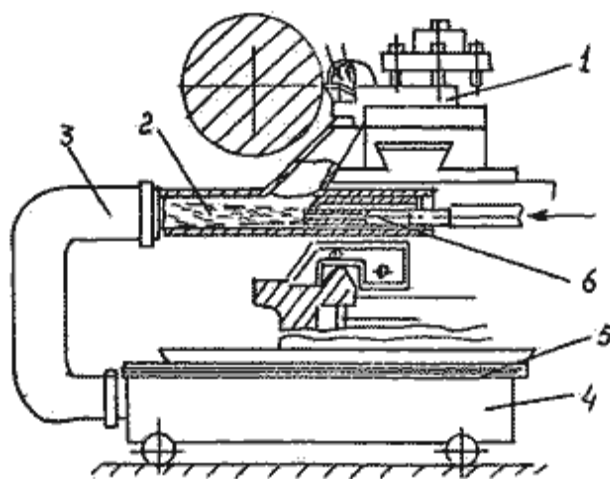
Ежекційний пристрій для токарно-гвинторізного верстата
